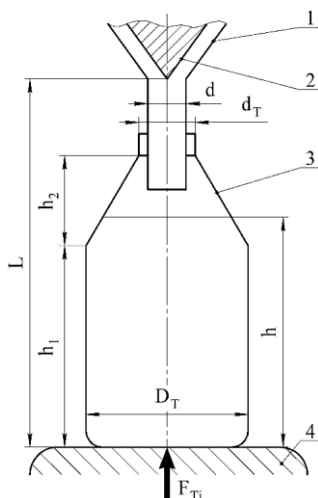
Схема формування дози продуктів пляшки циліндро-конічної форми: 1 — насадка фасувального пристрою; 2 — клапан; 3 — пляшка; 4 — зважувальний елемент
